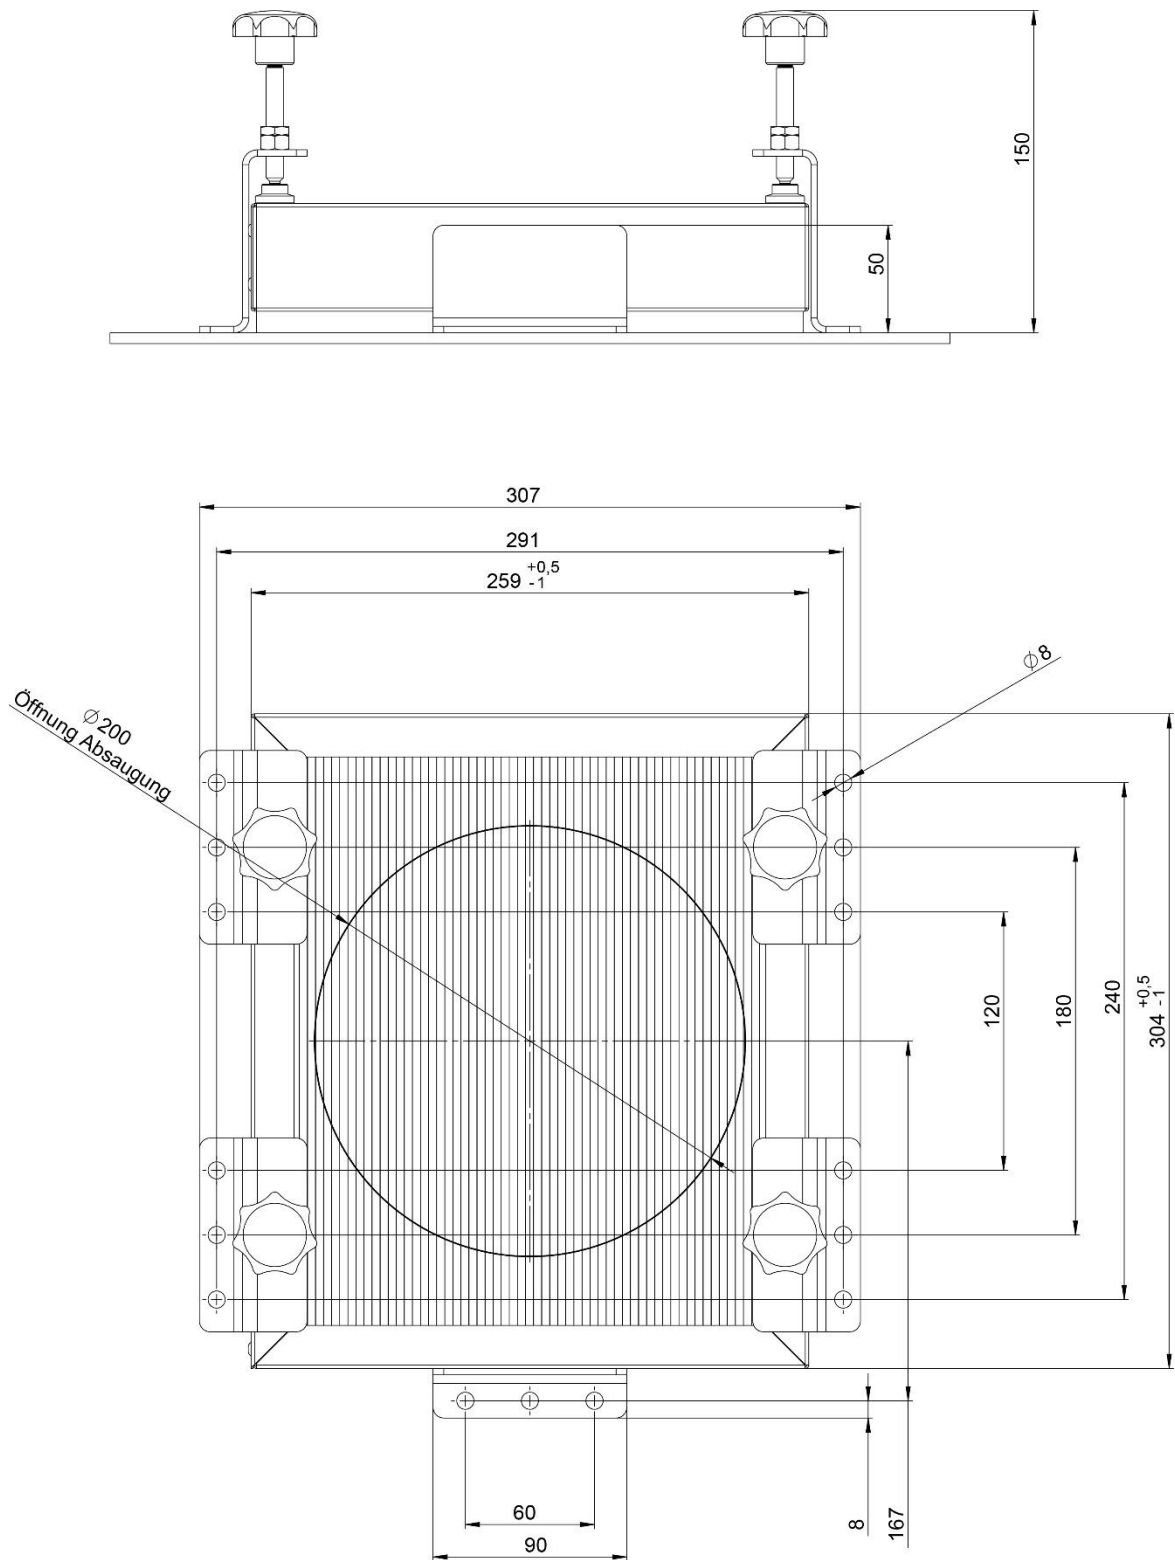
Einbau einer MIO Filterplatte in eine Bearbeitungsmaschine
